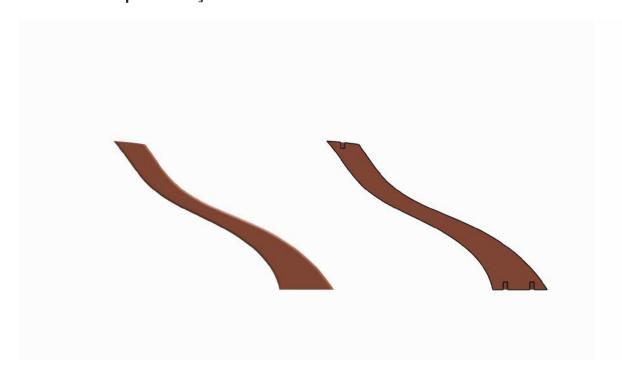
Detalhe em corte Suporte Braço - Furos para cavilhas
